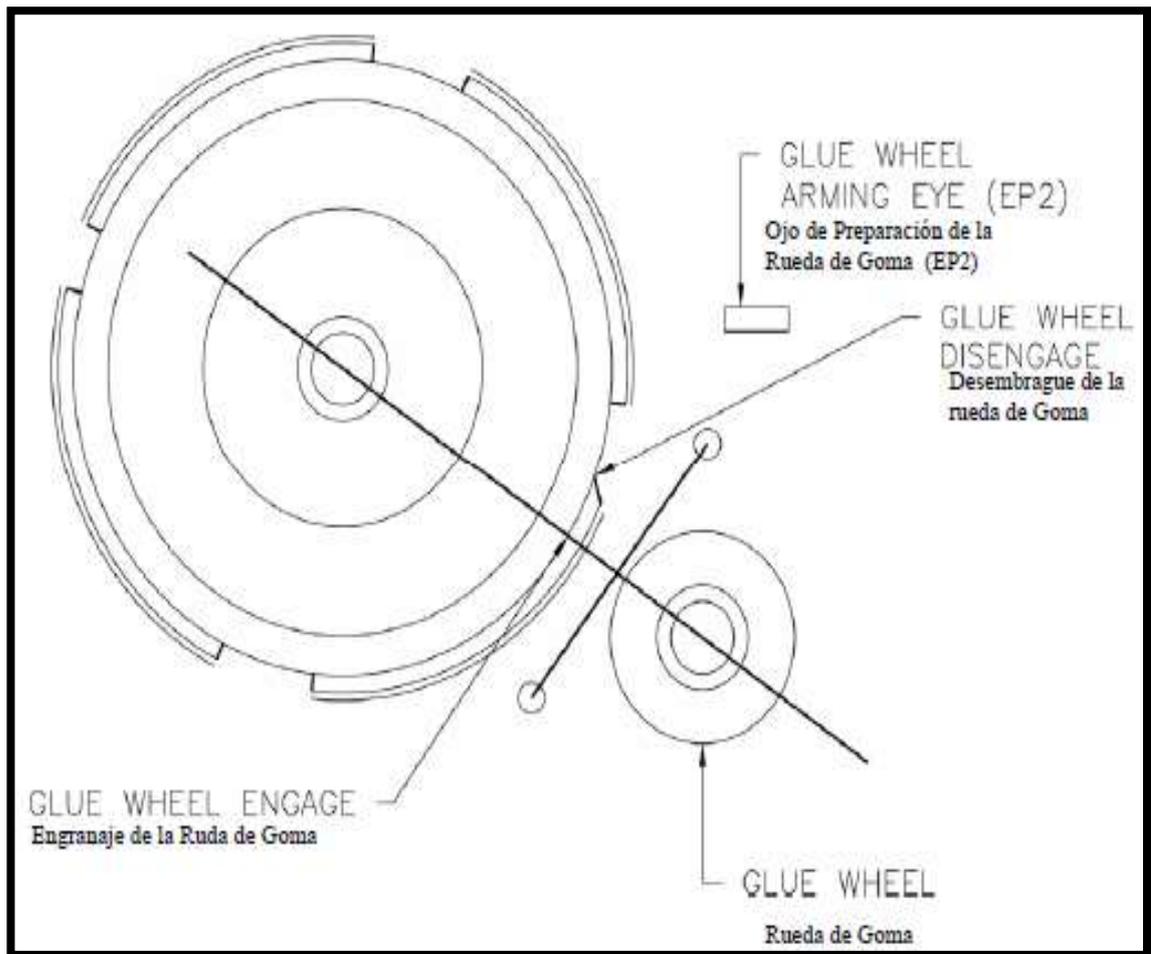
CRONOMETRAJE DEL ENGRANAJE DE LA RUEDA DE GOMA
